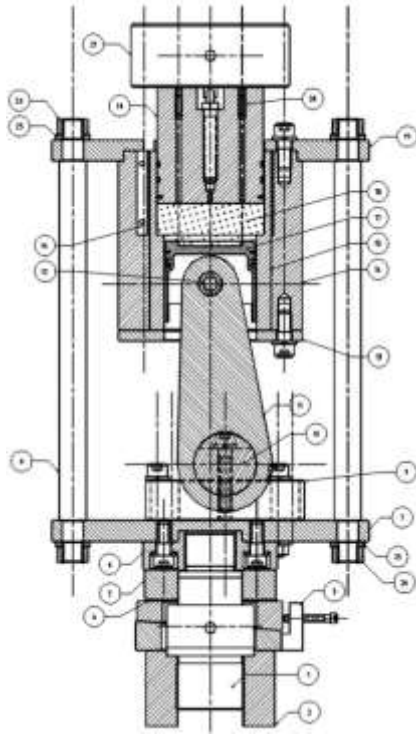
Dibujo de ensamble virtual del dispositivo para pruebas de fatiga y compresión para pistones de motores a gasolina
